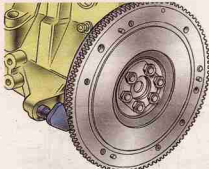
Проверка осевого свободного хода коленчатого вала
